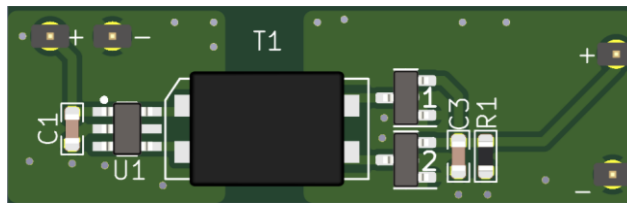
PCB 示意图(尺寸: 10.8 x 34.6mm)
